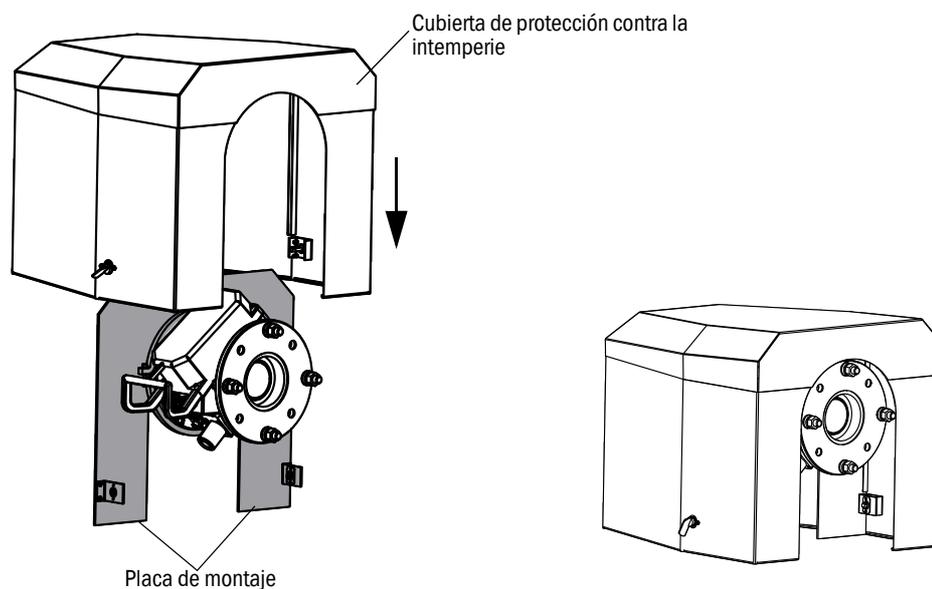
Montaje de la cubierta en el adaptador de aire de purga
